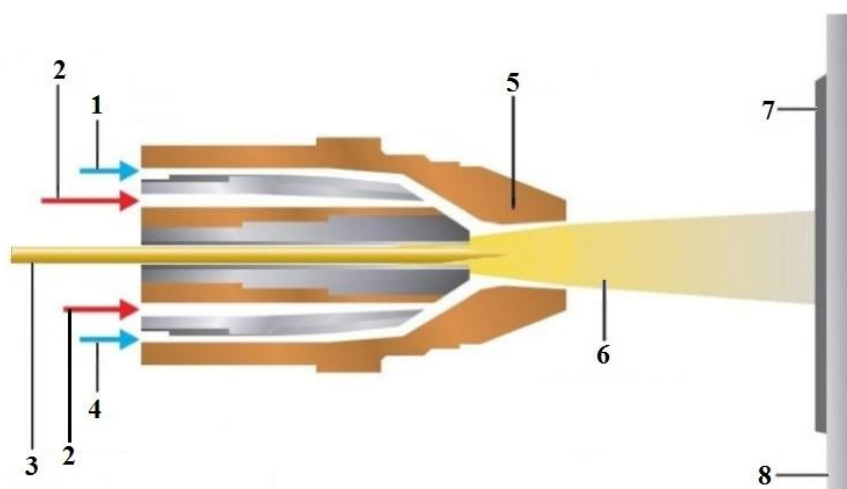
Схема газопламенного напыления проволокой или прутком
